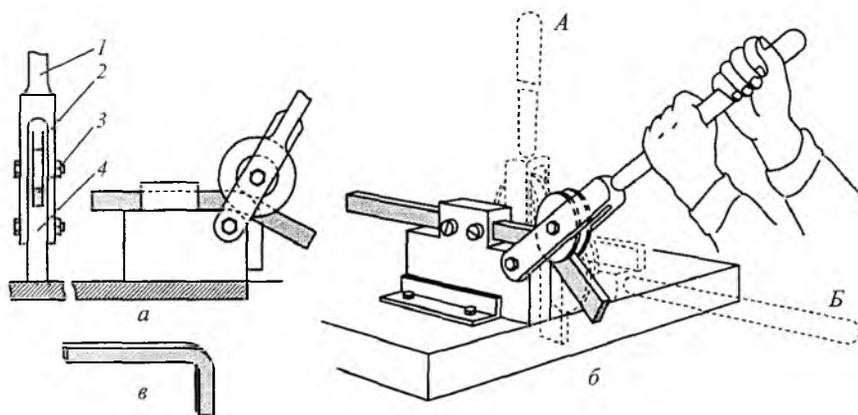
Приспособление для гибки рамки ножовочного станка:
